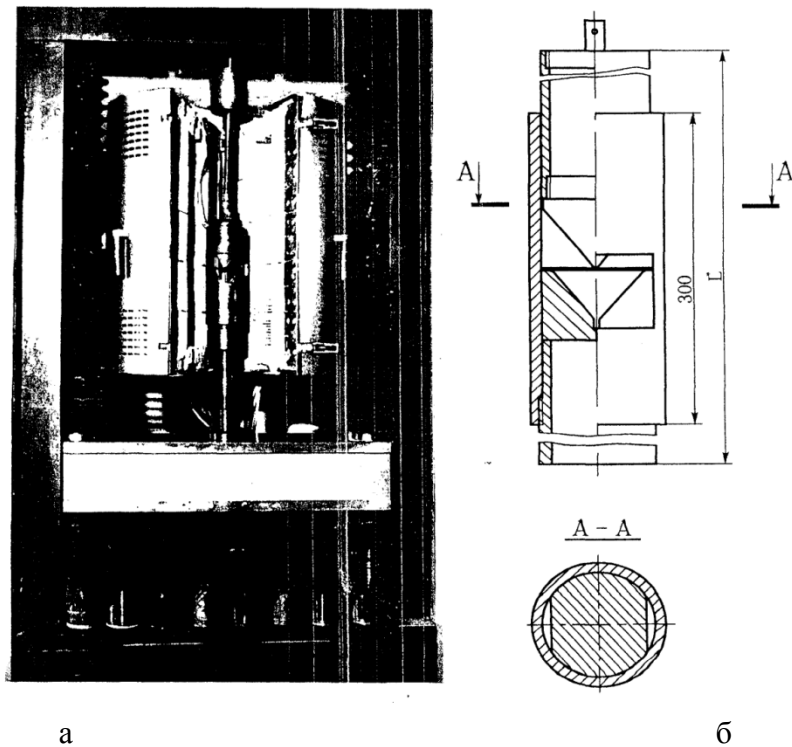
Приспособление для гибки образцов композита в нагретом состоянии:
